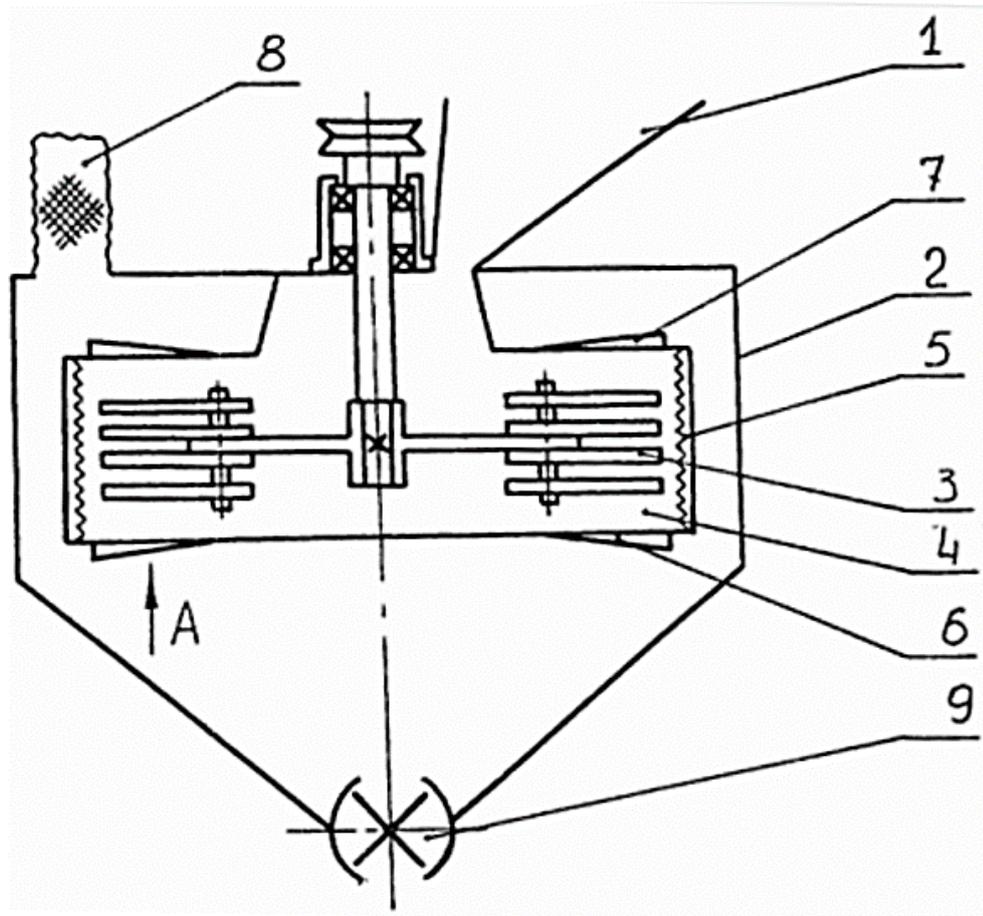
Молоткова дробарка із жалюзійними решетами: 1 – дозатор; 2 – корпус; 3 – молотковий ротор; 4 – дробильна камера; 5 – дека; 6, 7 – жалюзійні ґрати; 8 – фільтр; 9 - змішувач
